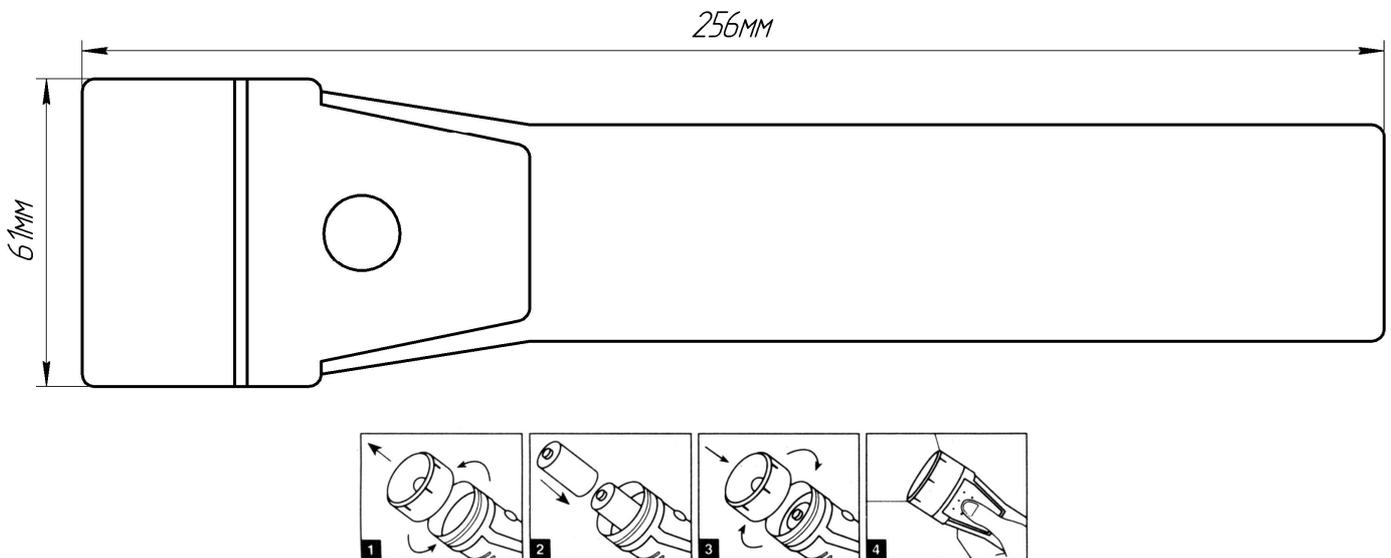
Внешний вид, габаритные размеры ППРИ-П-01
